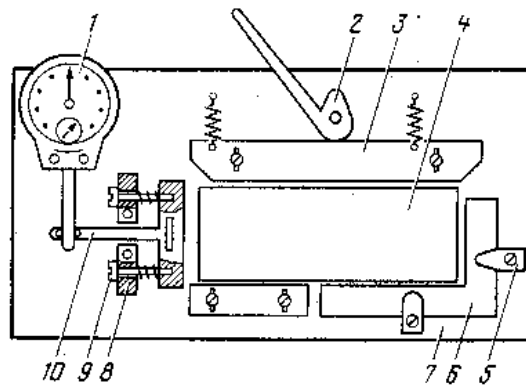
Приспособление для контроля размеров пластины: 1 — индикатор; 2 — зажим прижимной планки; 3 — прижимная планка пластины; 4 — контролируемая пластина; 5 — зажимы угольника; 6 — угольник; 7 — плита; 8 — стойка двухплечего рычага; 9 — винт двухплечего рычага; 10 — рычаг индикатора
